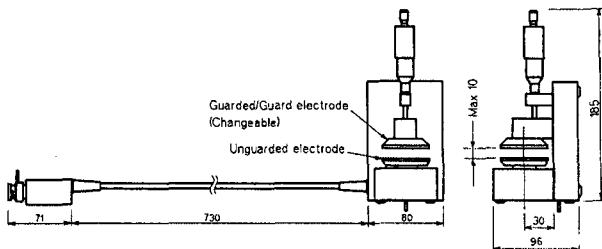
Dimensions of Agilent 16451B dielectric test fixture assemble
